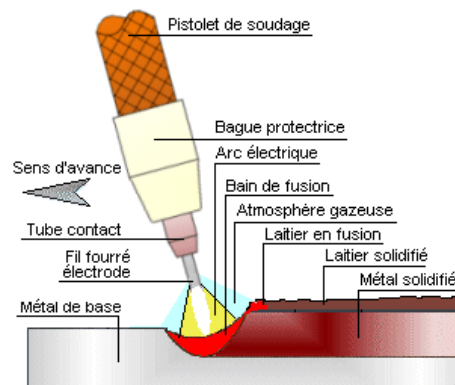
soudage MAG fil fourré sans gaz. [8]
